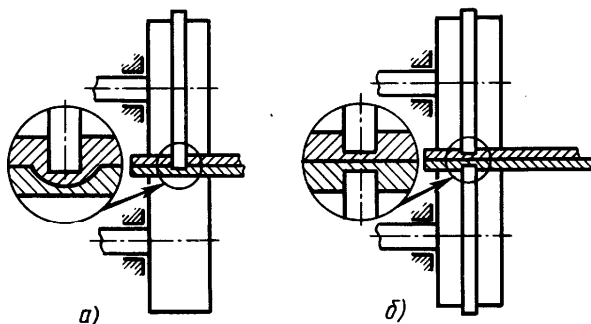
Схема шовной холодной сварки: а - с односторонним; б - с двусторонним деформированием
